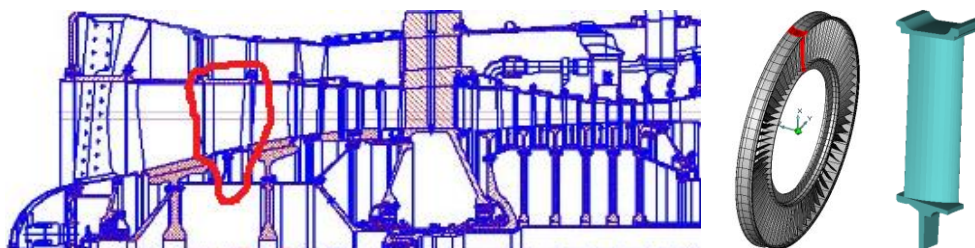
Продольный разрез ГТД НК-16 (фрагмент), ступень компрессора и лопатка
